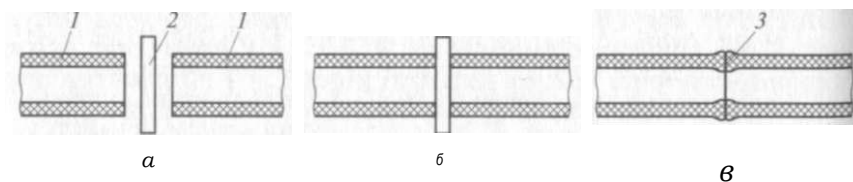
Схема сварки труб встык с применением плоского нагревательного инструмента:
